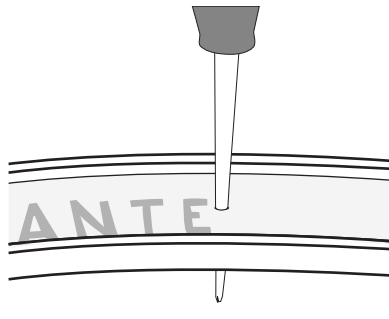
Das Felgenband mit dem Werkzeug durchstoßen, um ein Ventilloch herzustellen.
